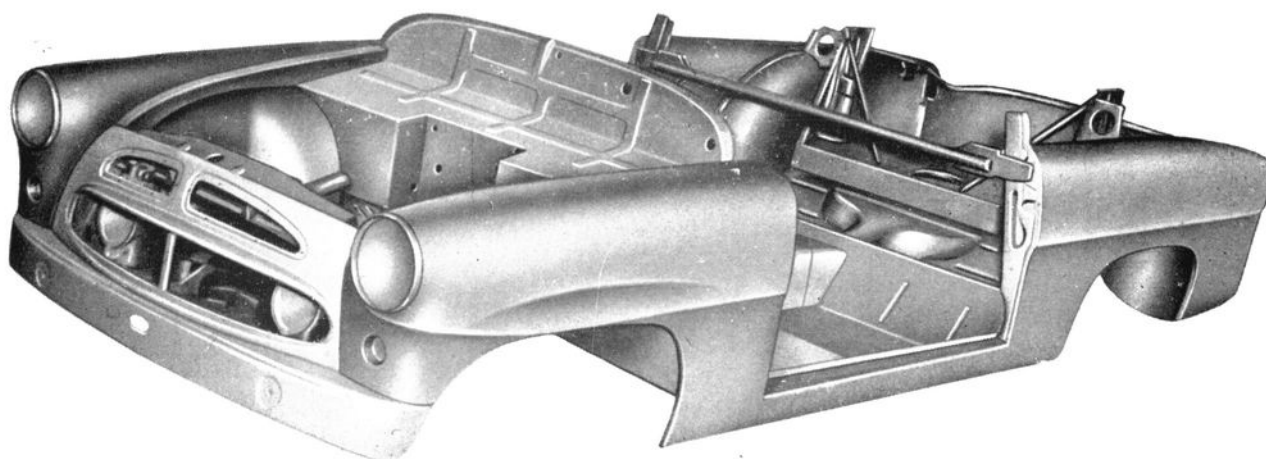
Úplný přední díl karosérie (s namontovaným úplným spodním dílem masky chladiče a maskou).
